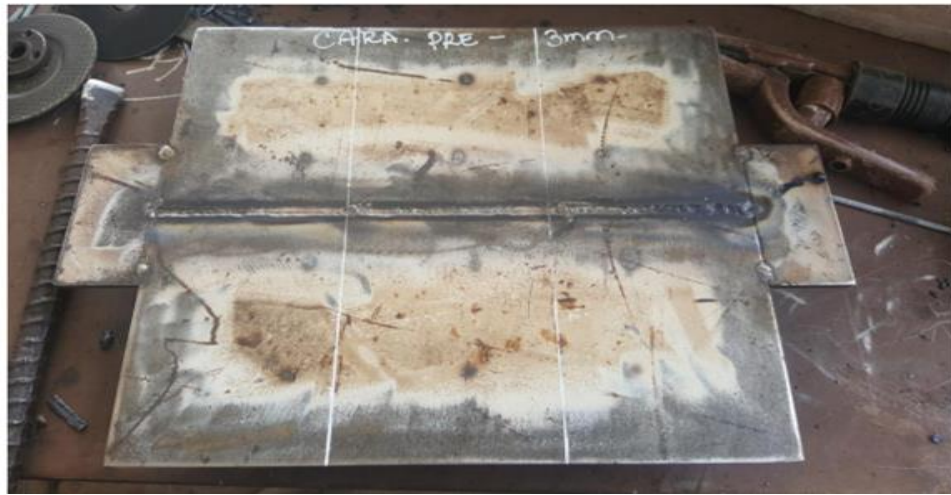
Probeta de soldadura, Acero MIL-DTL46100E, Cara superior
